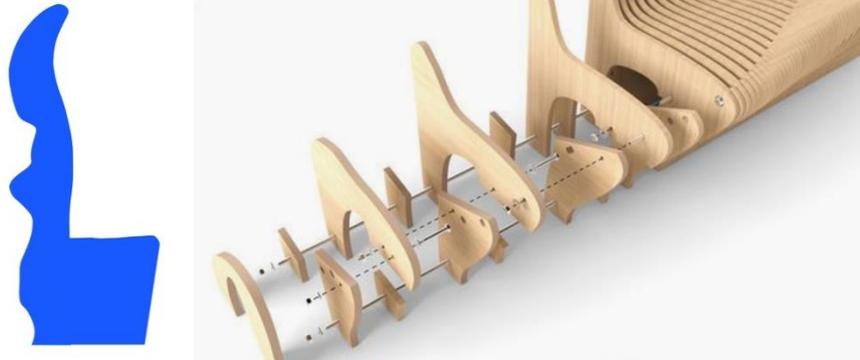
Coupe du second principe constructif (hauteur : 1,4 m) accompagnée d'une photo d'assemblage.
